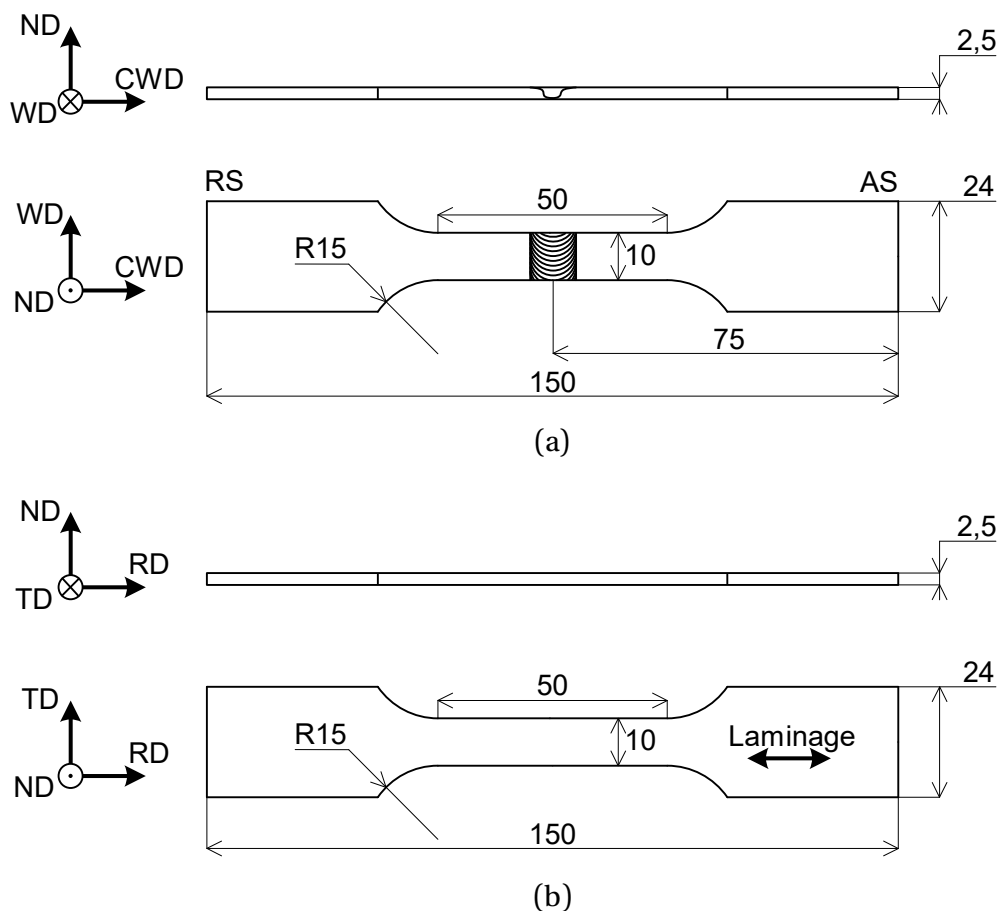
Géométrie des macro-éprouvettes de traction (a) tôles soudées, (b) matériaux de base.
